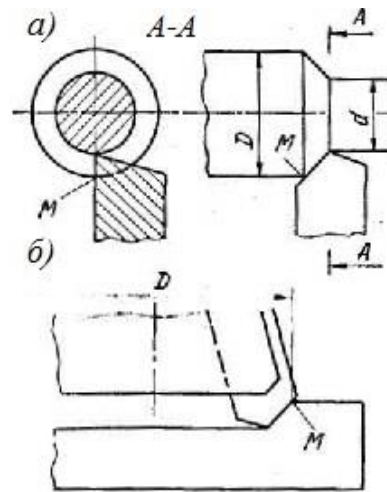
Схема вибору точки ріжучої кромки для визначення швидкості різання:
